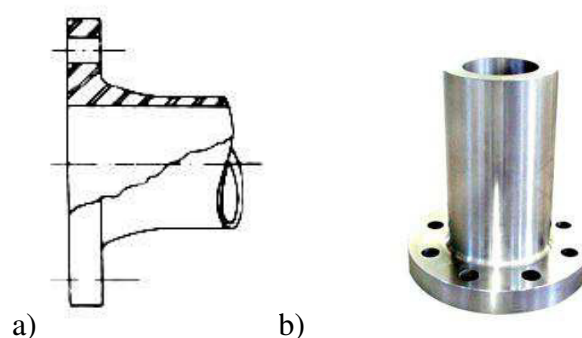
a) Desenho Representativo de um Flange Integral (SENAI, 1997) b) Flange Integral (AHAD Tubeline co., 2012)
